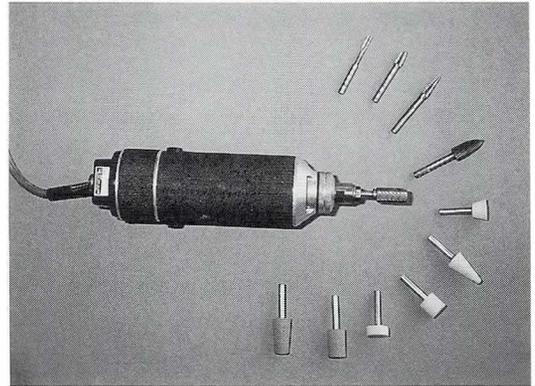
開先加工及び溶接ビード仕上用リユータ
